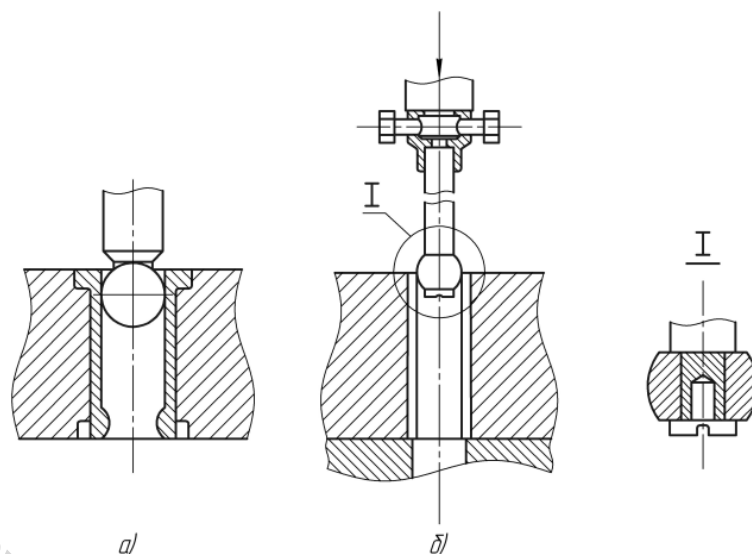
Калибрование подшипников в виде втулок после их запрессовки
